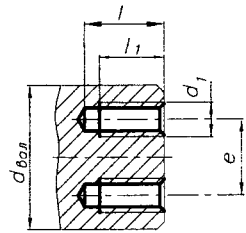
Размещение двух отверстий в сечении вала
